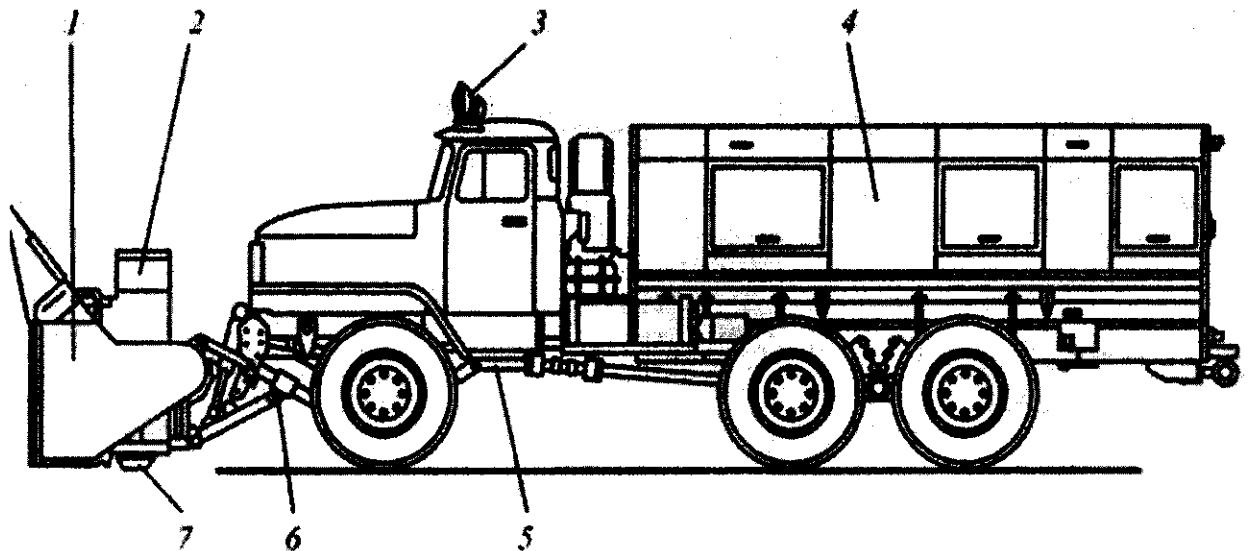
Шнекороторный снегопогрузчик на базе автомобиля Урал-4320-10 (1 - шнекороторное оборудование; 2 - направляющий аппарат снегометателя. 3 - фары рабочего освещения. 4 - моторный отсек, 5 - раздаточная коробка; 6 - рычажный механизм подвески шнекороторного оборудования, 7 - опорная лыжа)
